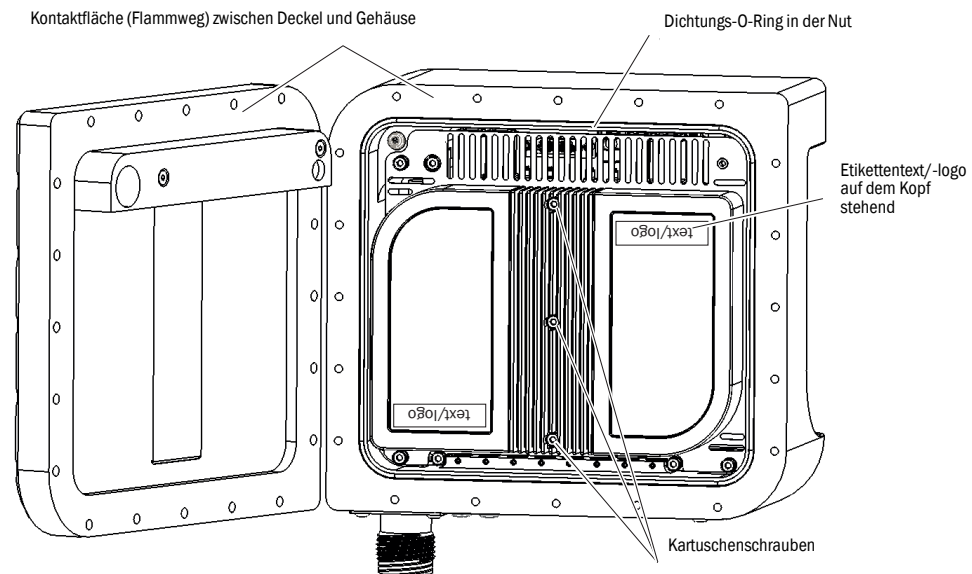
Geöffnetes Gehäuse mit Blick auf die Kartusche
